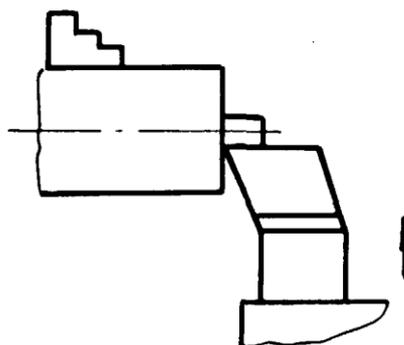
Схема обработки с движением подачи в поперечном направлении
